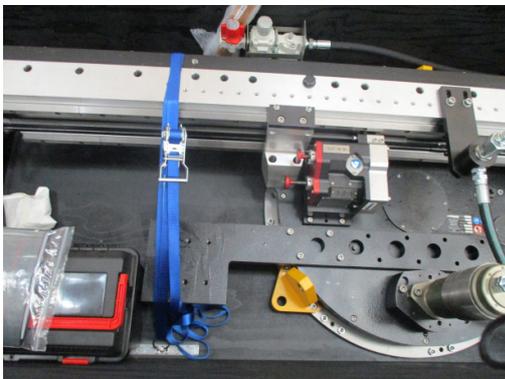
Cassa di stoccaggio 1 con gruppo macchina
